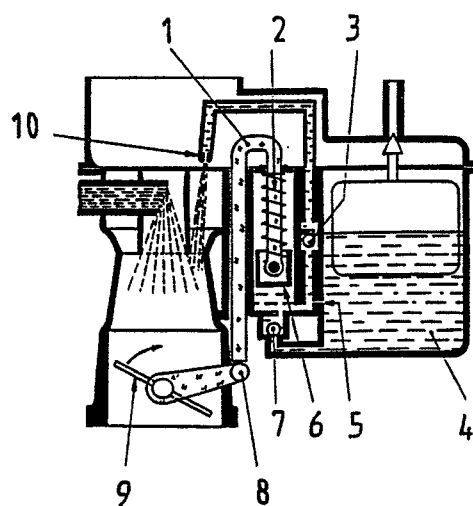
[2] — Carburatore munito di pompa di ripresa a stantuffo a comando meccanico.
